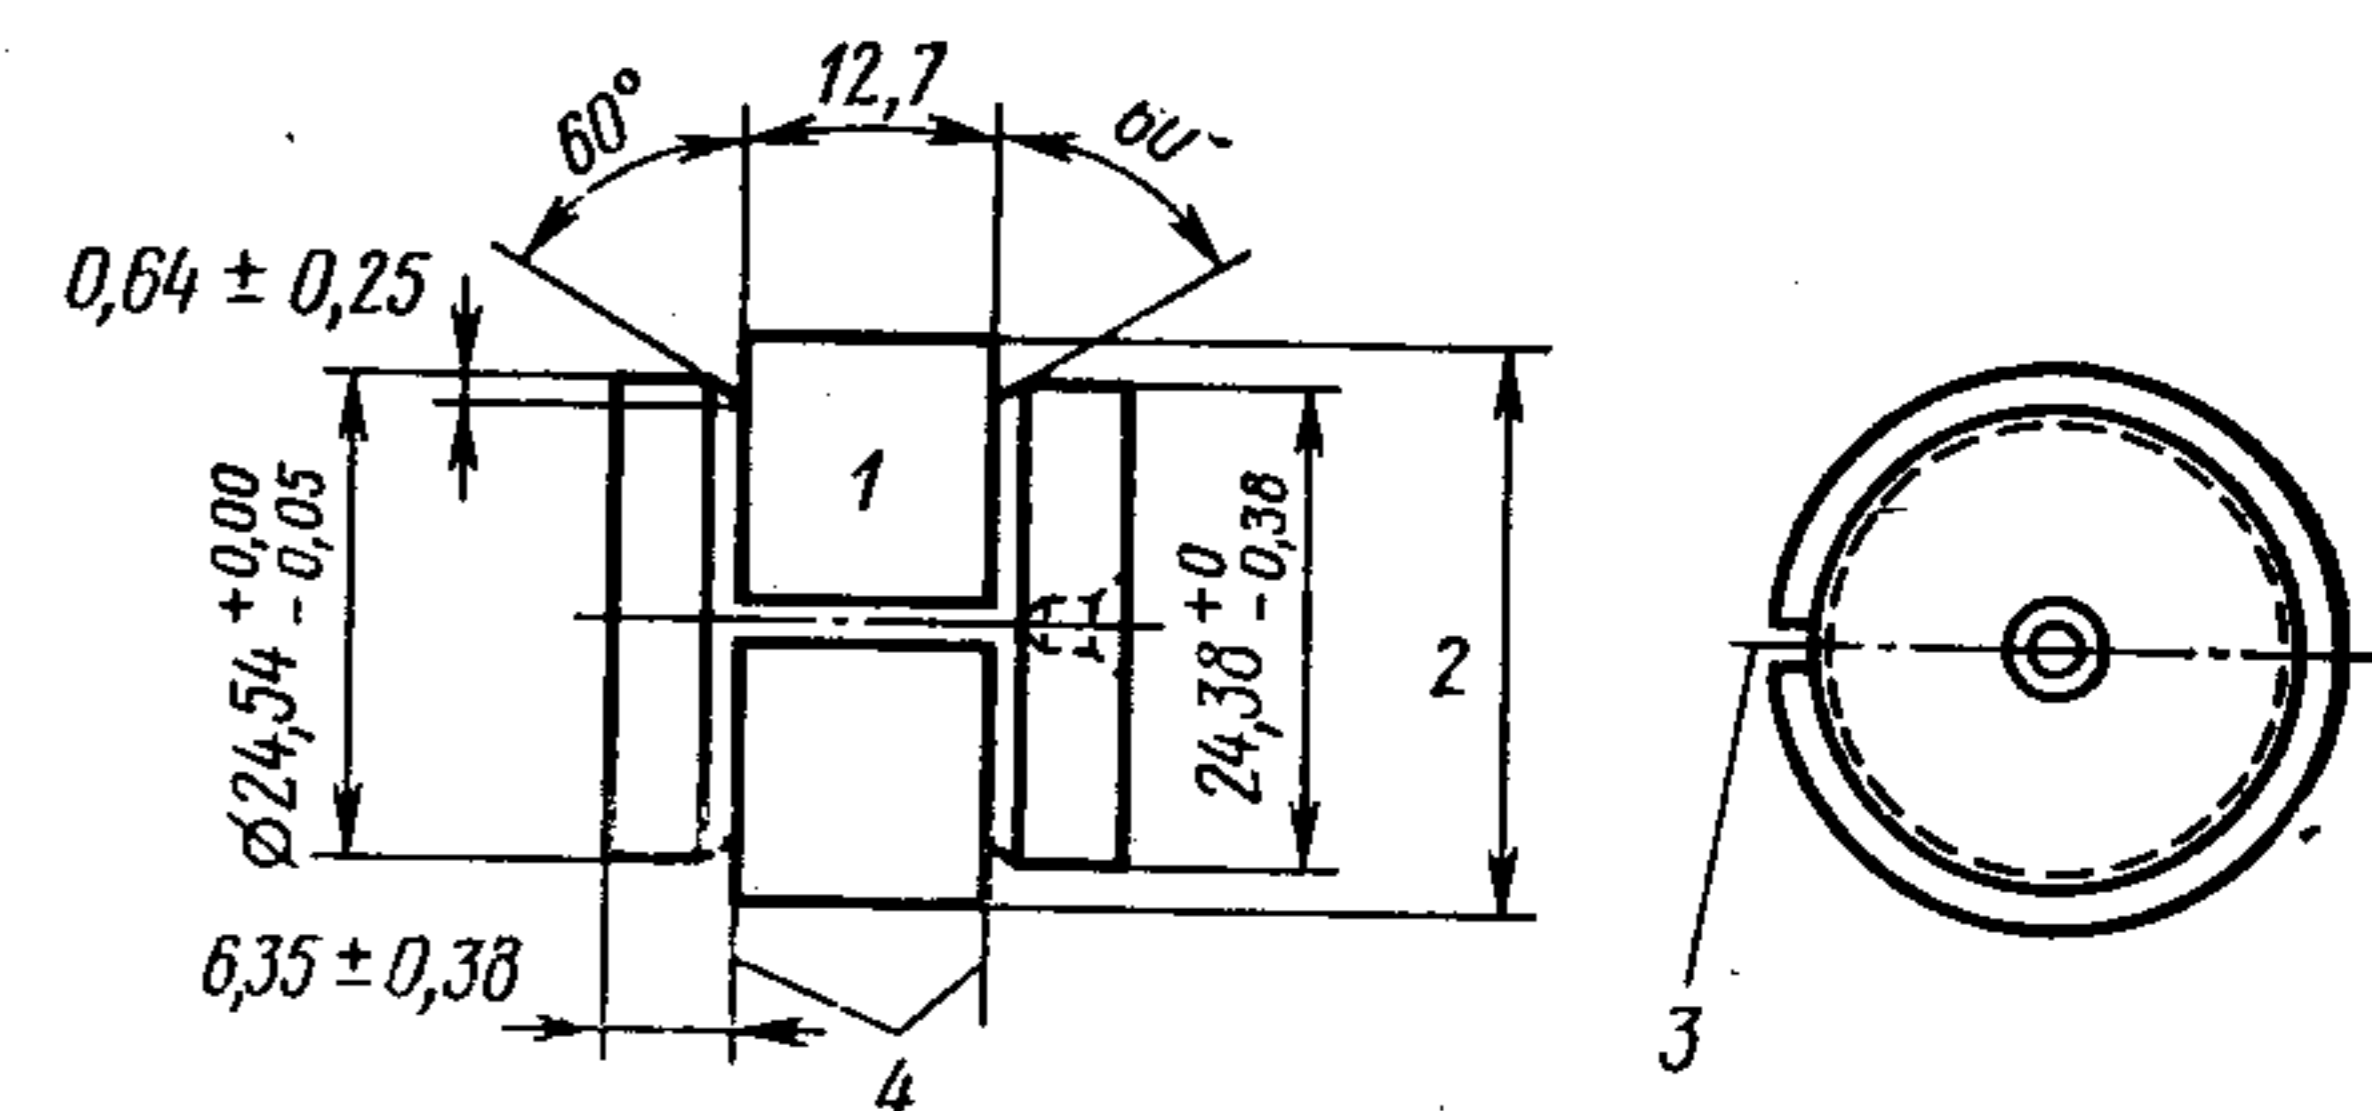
Размеры образцов для испытания на прочность сцепления при сдвиге:
